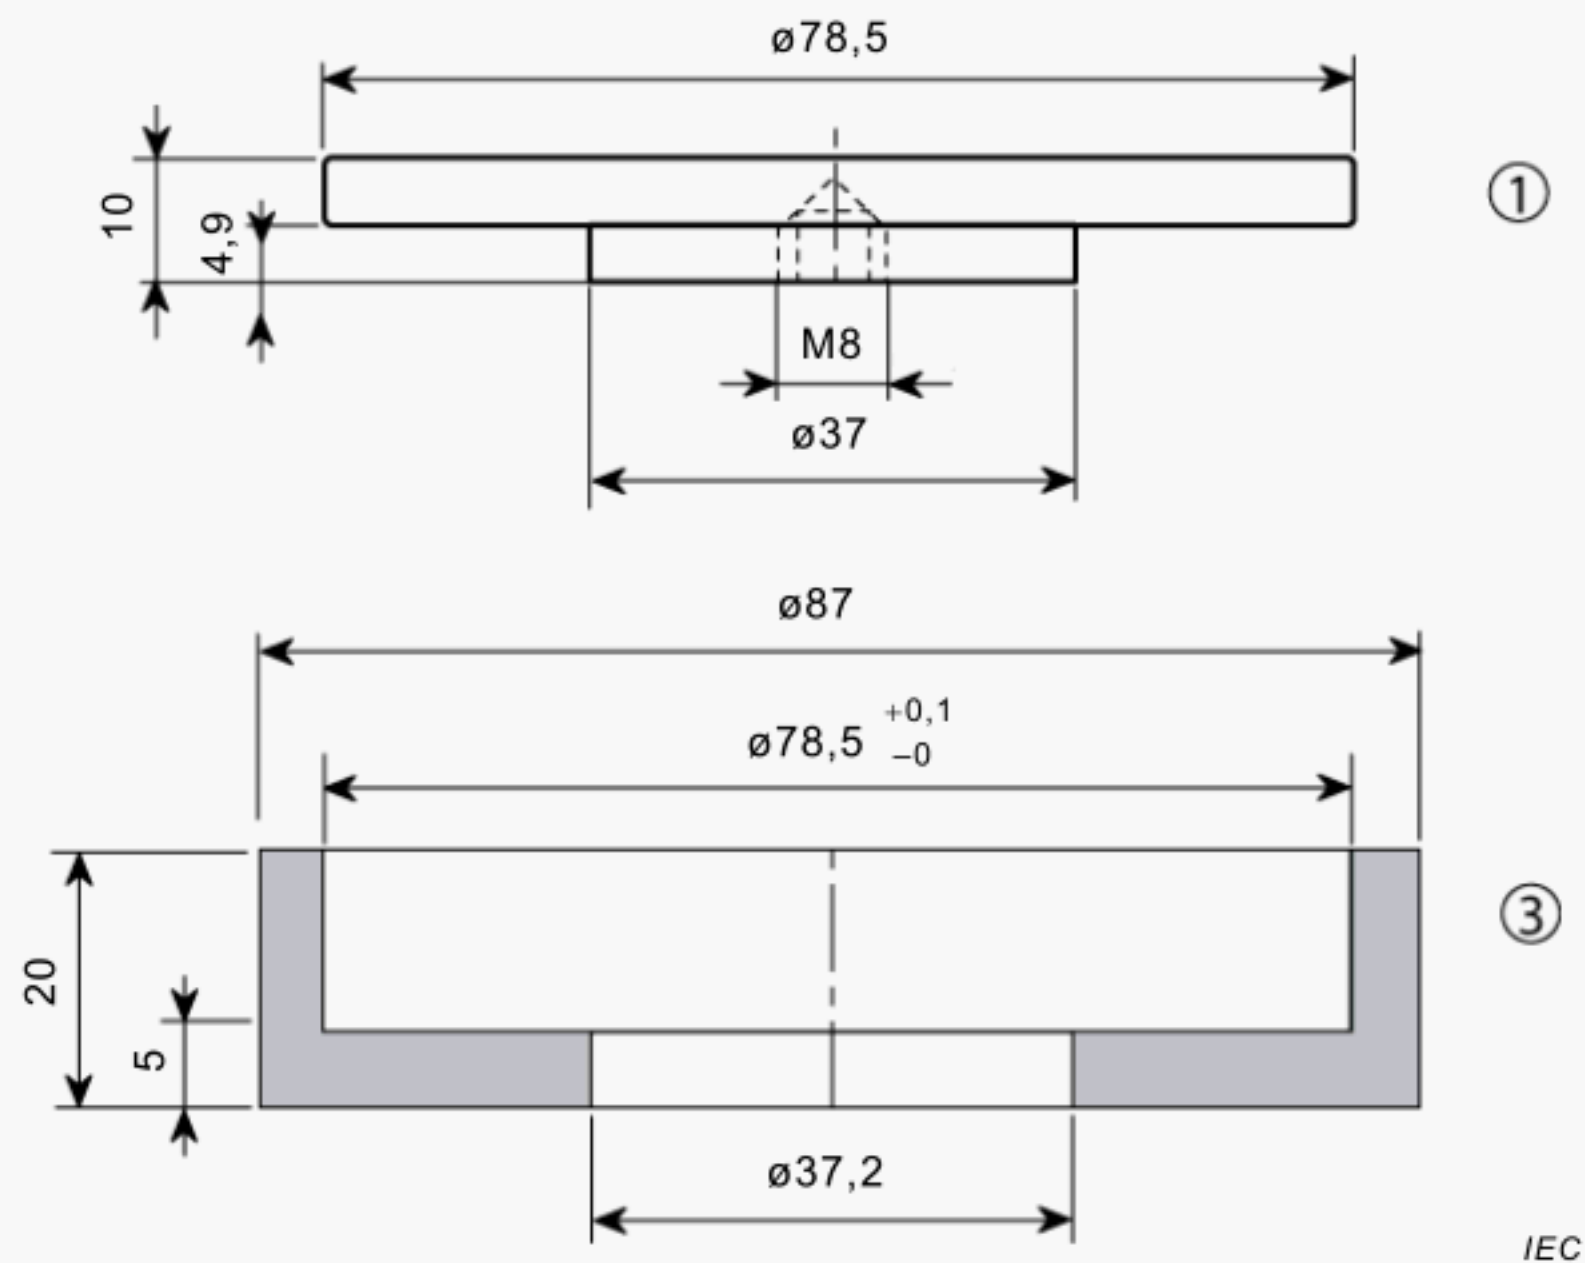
Pour tube rempli de mousse de 77 mm de diamètre
